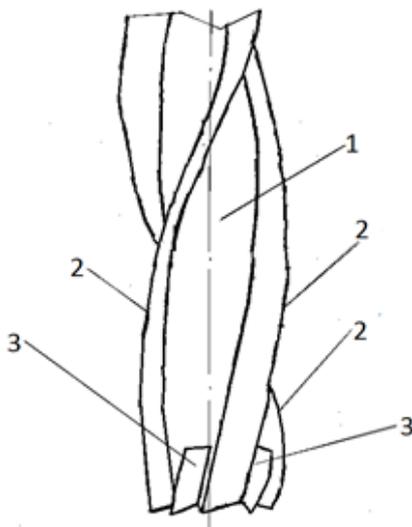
Длиннокромочная концевая фреза с дополнительно установленными зубьями в торцевой части: 1 – корпус фрезы; 2 – зубья основной части фрезы; 3 – дополнительно установленные специальные зубья в торцевой части
